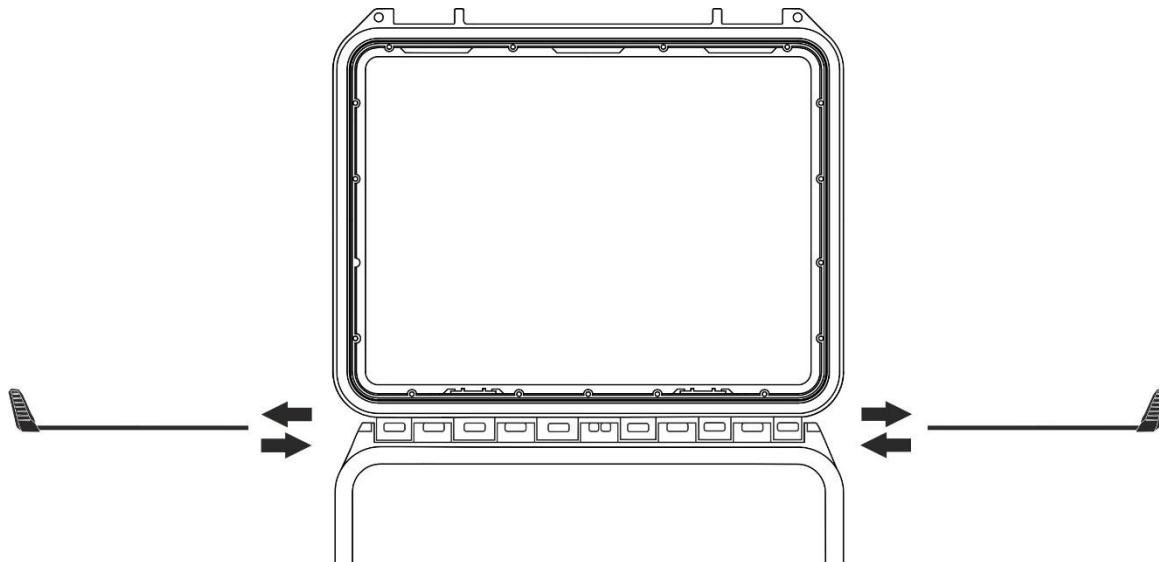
Remoção da tampa da caixa de instrumento - Passo 2
